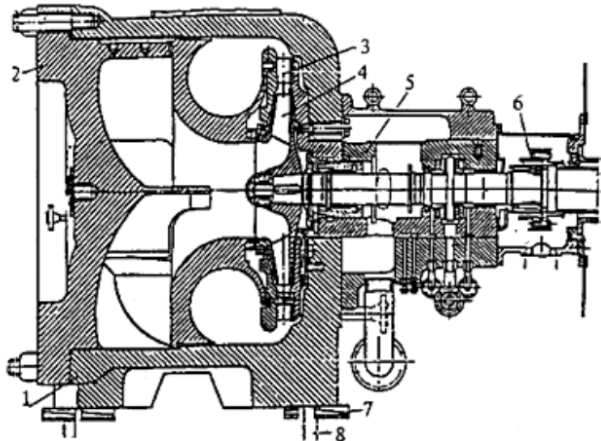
Неполнонапорный одноступенчатый нагнетатель 370-18 агрегата ГТК-10-4
